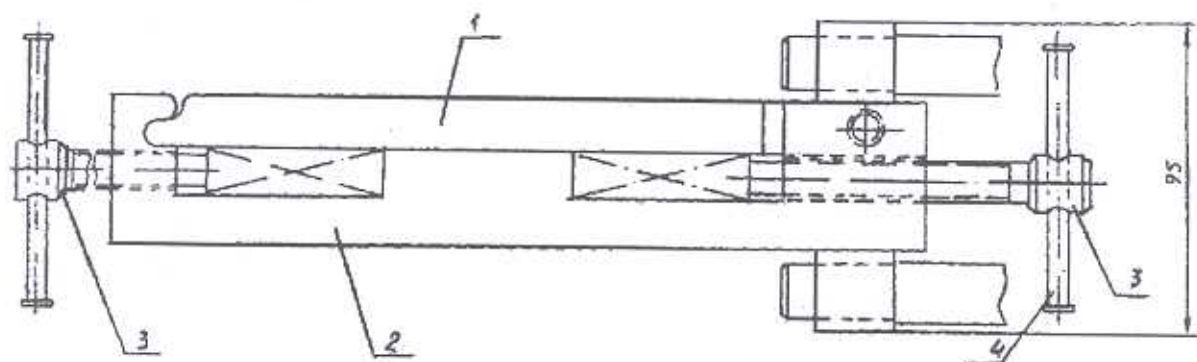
Приспособление для формовки головок стержней обмотки статора
